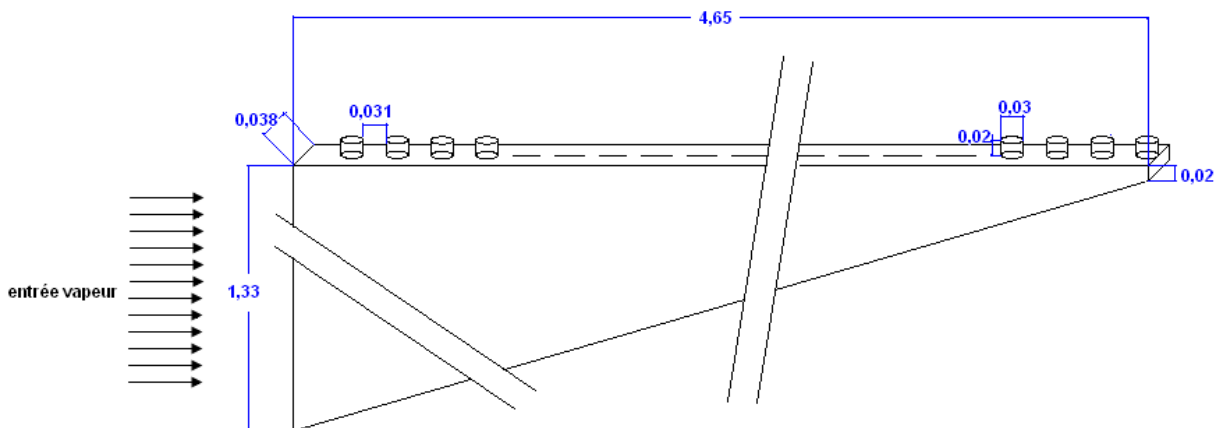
Premier tube distributeur à gauche (à 75 ouvertures) – dimensions en m
